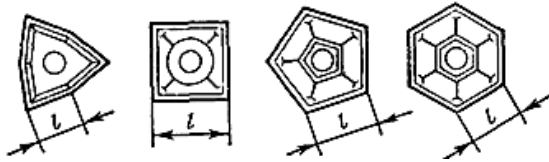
Формы твердосплавных механически закрепляемых пластин
